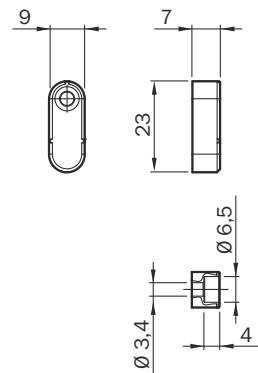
Maßzeichnung STR1 Betätiger "Mini"
